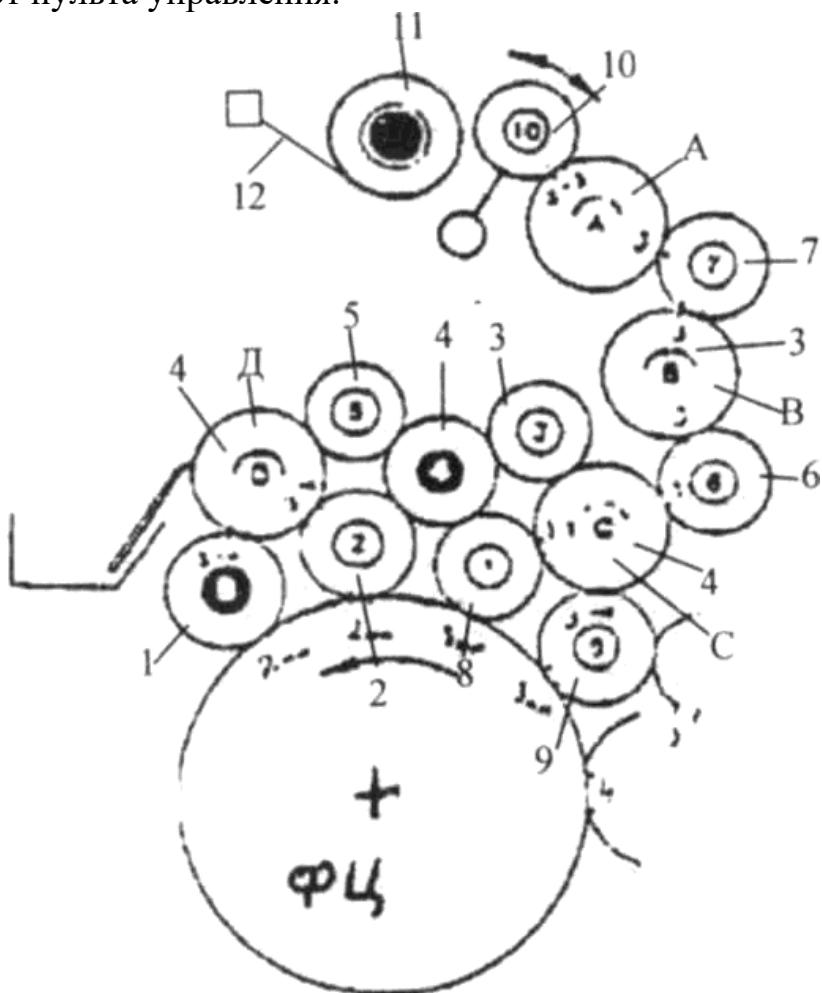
Красочный аппарат: Ф.Ц. — формный цилиндр; 1, 2, 8, 9 — накатные валики; 3, 4, 5, 6, 7, А, В, С, Д — раскатная система; 10 — передаточный валик; 11 — докторный цилиндр; 12 — красочный ящик; 10, 11, 12 — питающая группа
